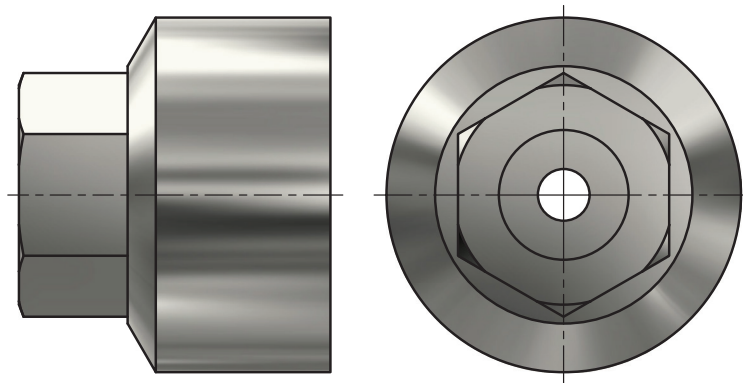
Расположение детали для оформления главного вида и вида слева
